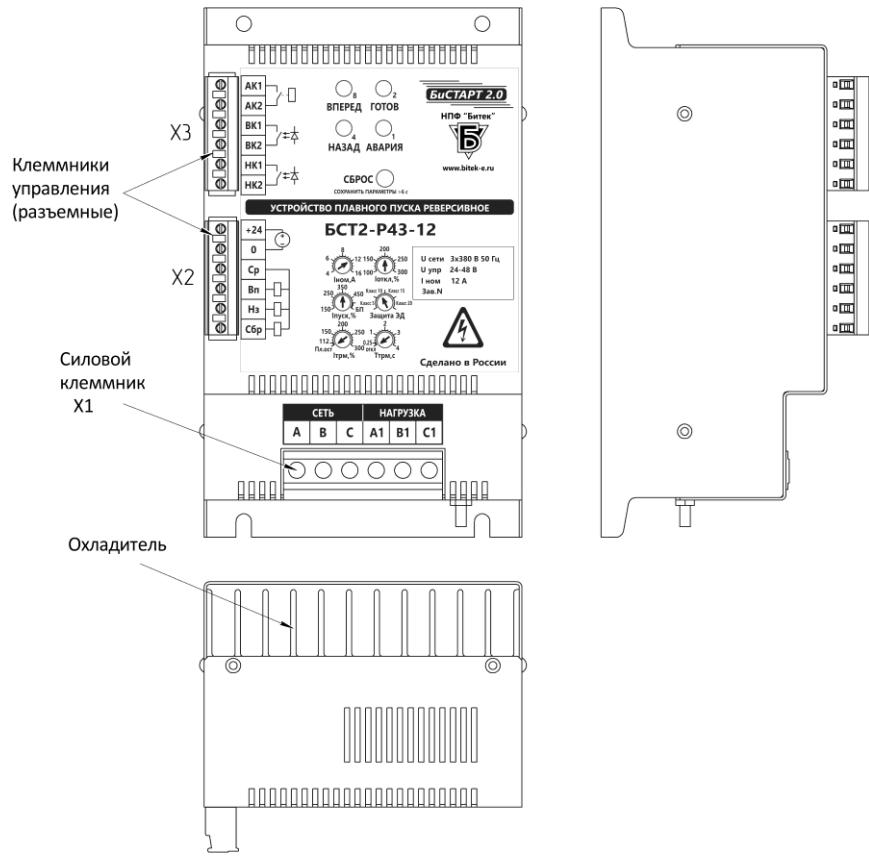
Внешний вид пускателя БСТ2-Р43-12
